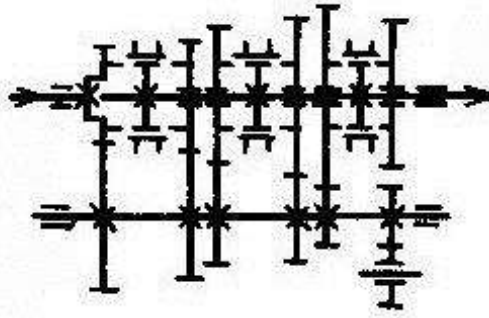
Кинематическая схема трехвальной коробки передач
